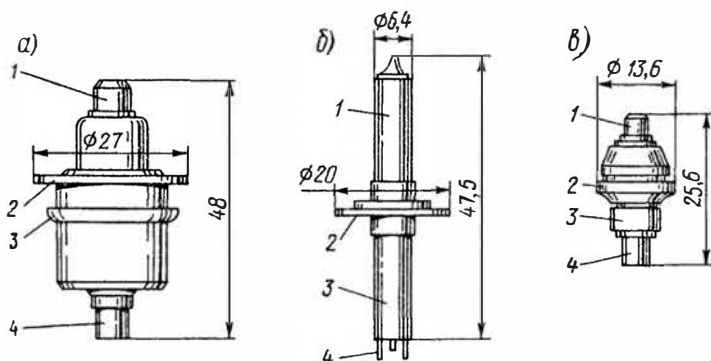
Триоды для СВЧ: а — металlostеклянный; б — «карандашный»; в — сверхминиатюрный металлокерамический
